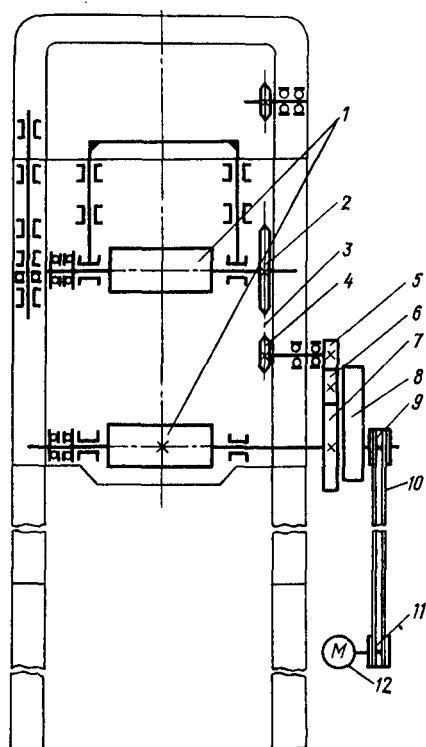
Кинематическая схема механизма подачи лесопильной рамы 2Р75-1:
